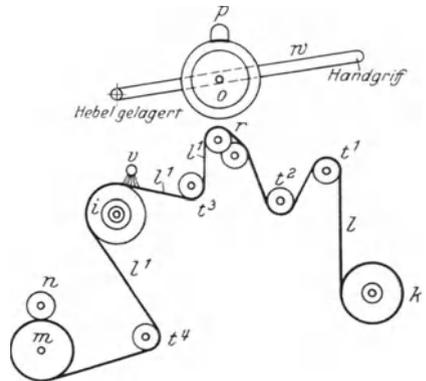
Schnitt durch die Chenilleschneidmaschine.
